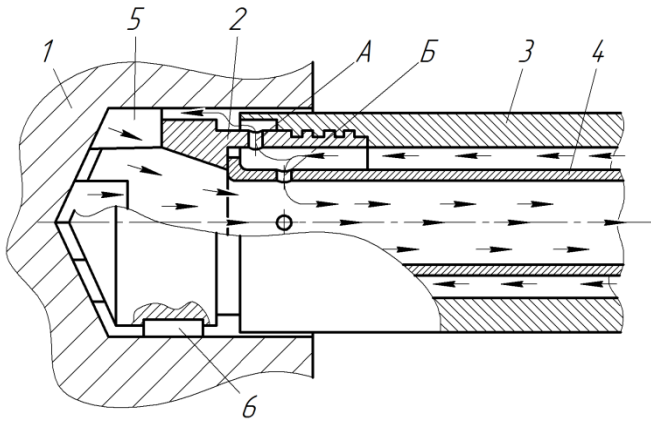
Ежекторне свердління з циліндричними напрямними
